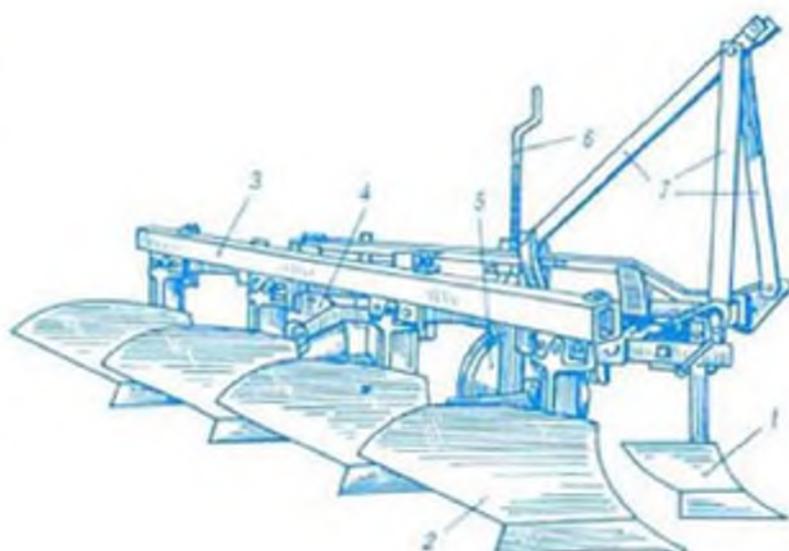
Плуги. Навесной лемешный тракторный плуг: 1 — предплужник; 2 — корпус; 3 — рама; 4 — дисковый нож; 5 — опорное колесо; 6 — винтовой механизм регулирования глубины пахоты; 7 — навеска плуга.
